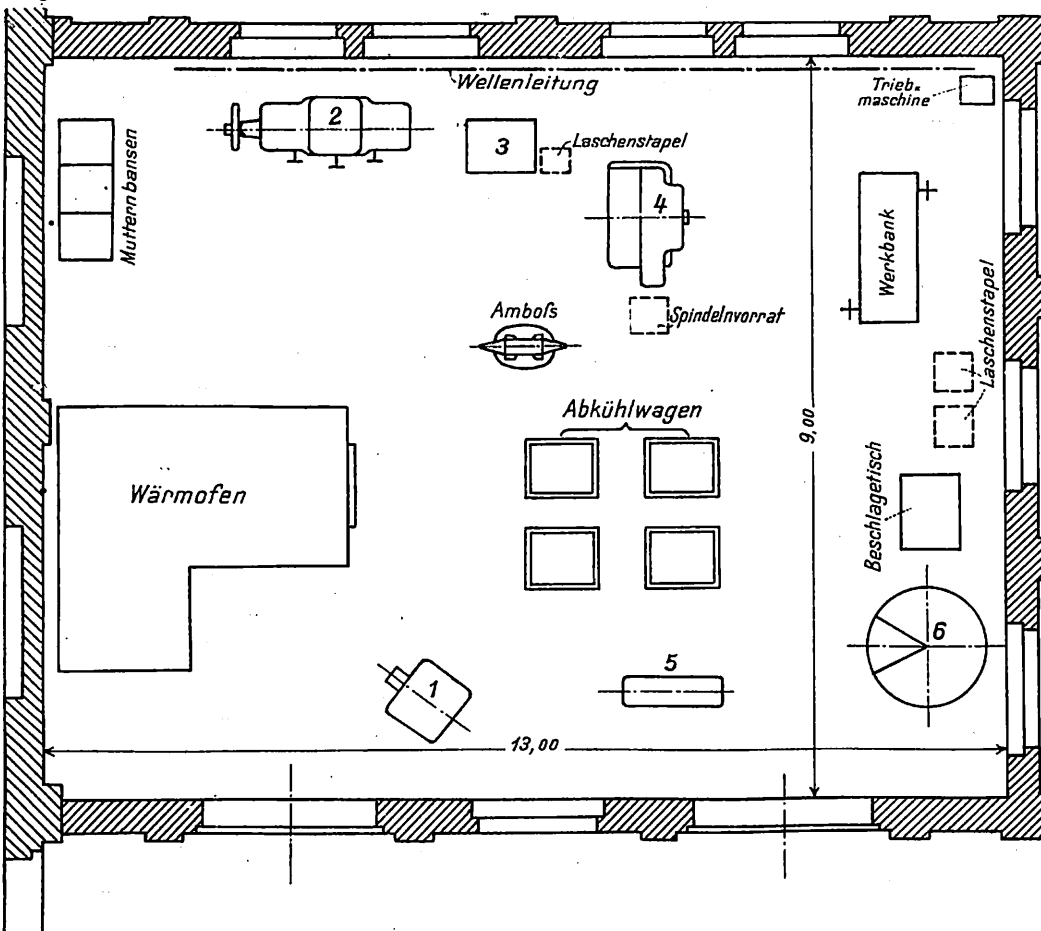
Grundriß einer neuen Anlage zur Wiederherstellung beschädigter Schraubenkuppelungen.
